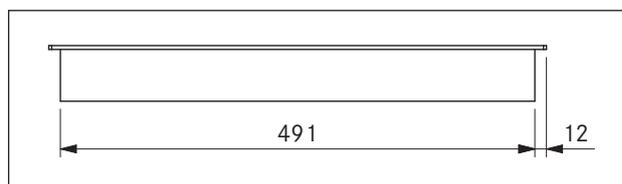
Dimensões do aparelho CKI, vista lateral
